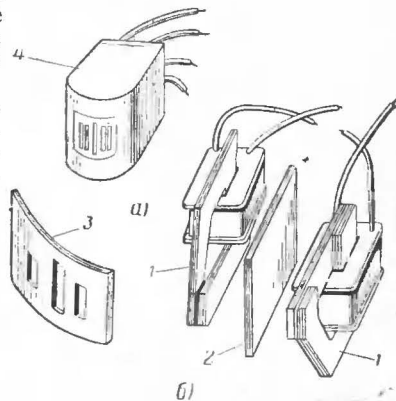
Комбинированная головка. а — внешний вид; б — устройство.
